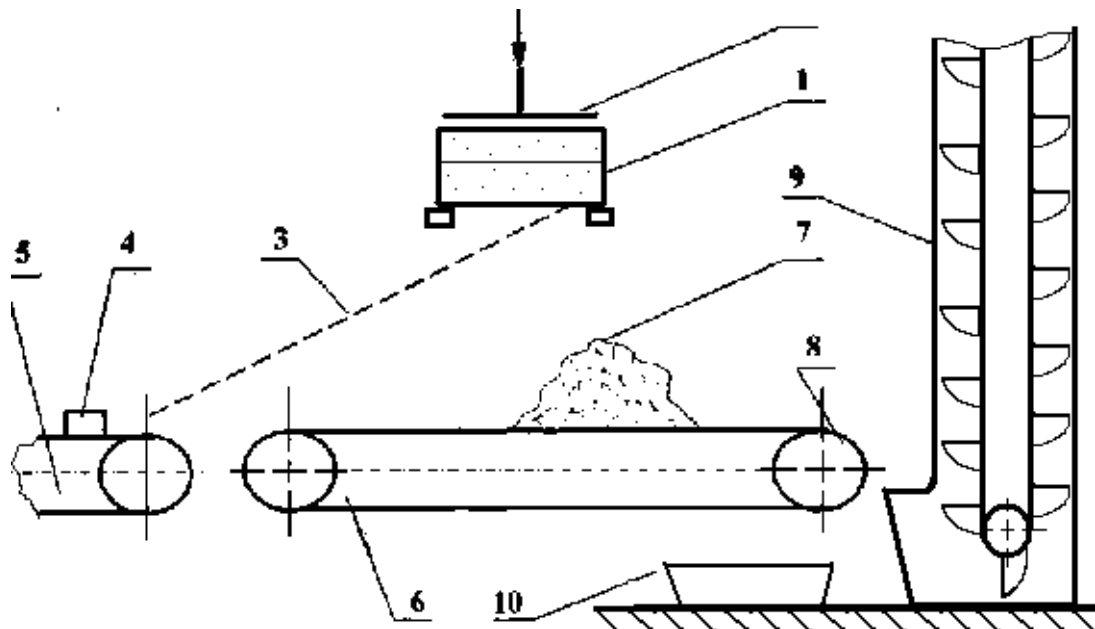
Схема вибивання відливок: 1 - форма; 2 - пресо́ва коло́дка, 3 - реші́тка-скрі́зь; 4 - ви́ливоч; 5 - пласти́нчастий транспортер; 6 - стрі́чковий транспортер; 7 - горі́ла зе́мля, металеві вклю́чення; 8 - шкі́в з електромагні́том; 9 - е́леватор; 10 – ко́роб
